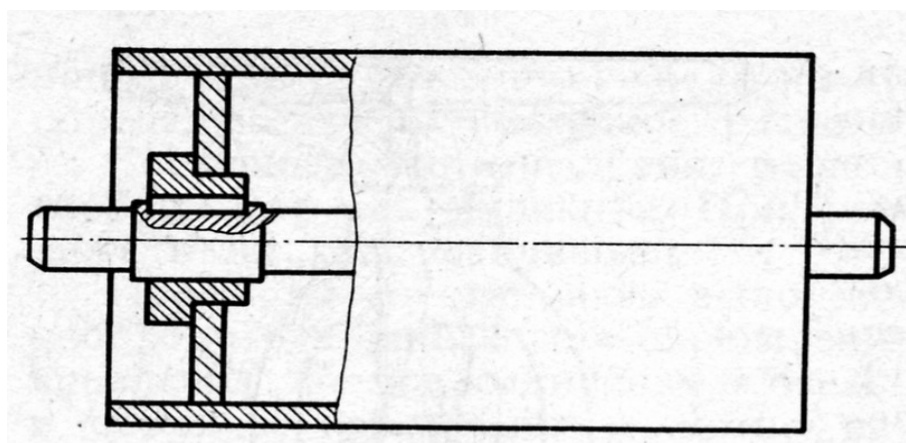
Штриховка в сечениях однородного материала в неподвижных соединениях на сборочном чертеже
